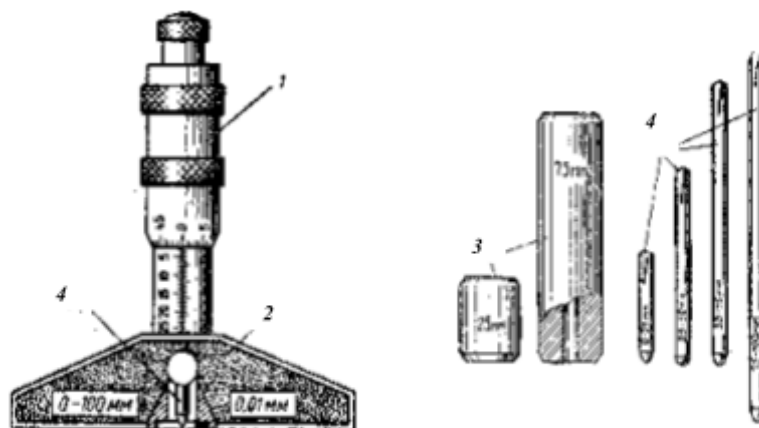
Мікрометричний глибиномір: 1 – головка глибиноміра; 2 – основа; 3 – установочні міри; 4 – вимірювальні стрижні
